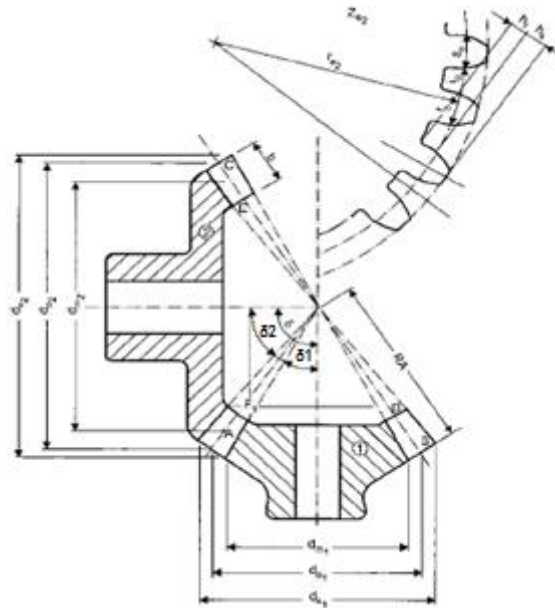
Detalhe construtivo da engrenagem cônica de dentes retos [44].
